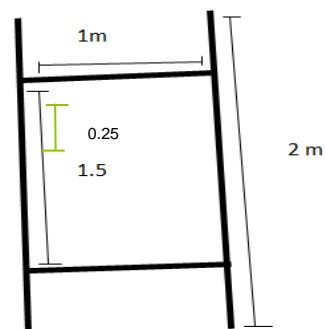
Zaranda Modelo CIMMYT y esquema de zaranda .
